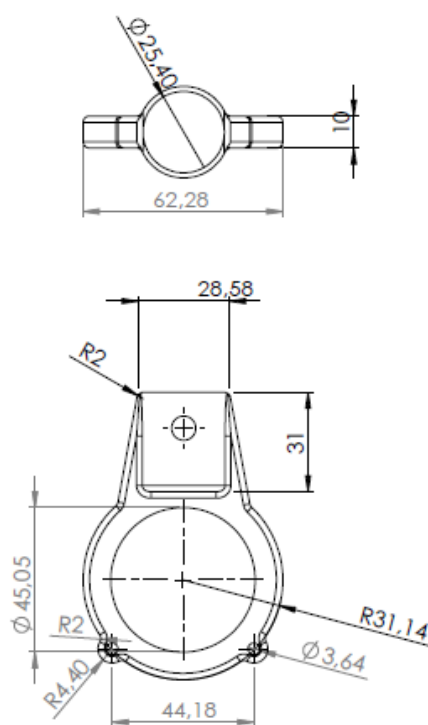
3D модель держателя мотора в SolidWorks
